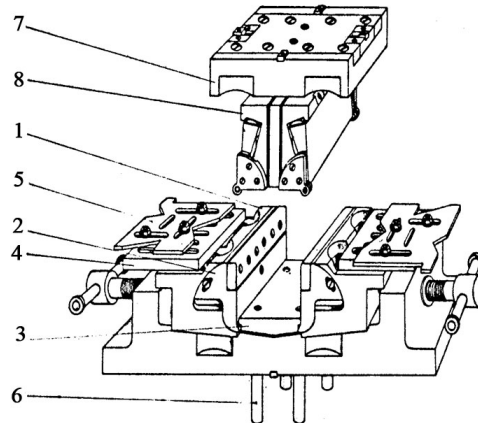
Сменный переналаживаемый пакет для двухугловой гибки деталей с заданными точностными параметрами расположения и формы поверхностей
